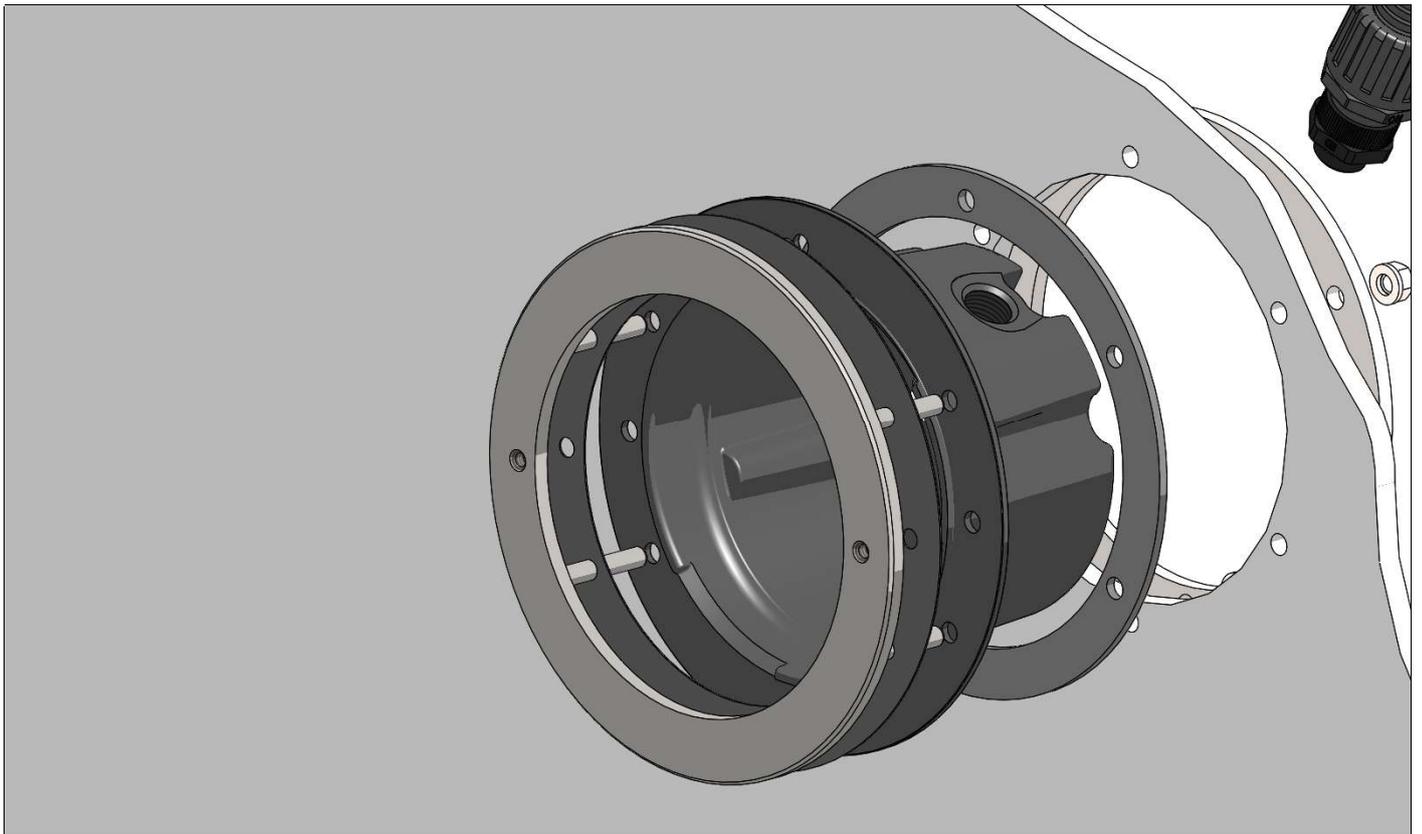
Ordre de montage Pièce à sceller bassin préfabriqué
